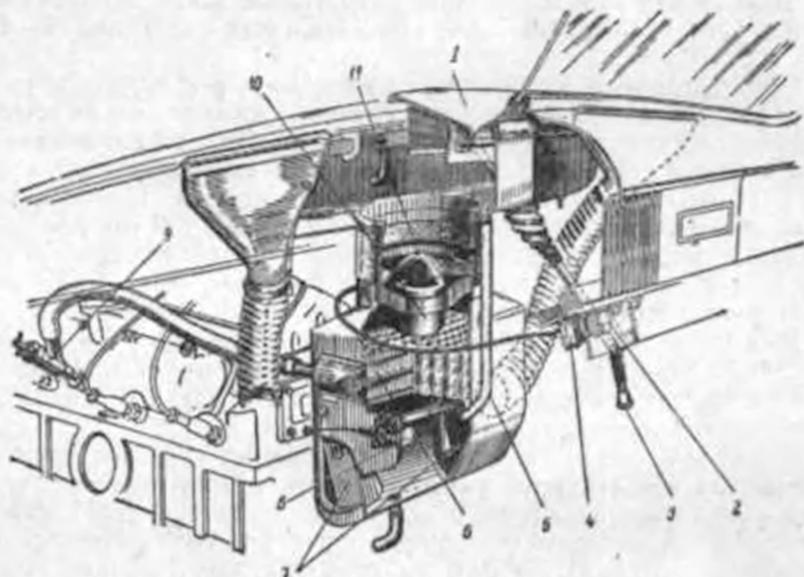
Отопитель кузова и обогреватель ветрового стекла
